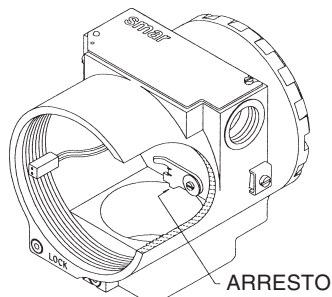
Dispositivo di fermo della rotazione sensore.
